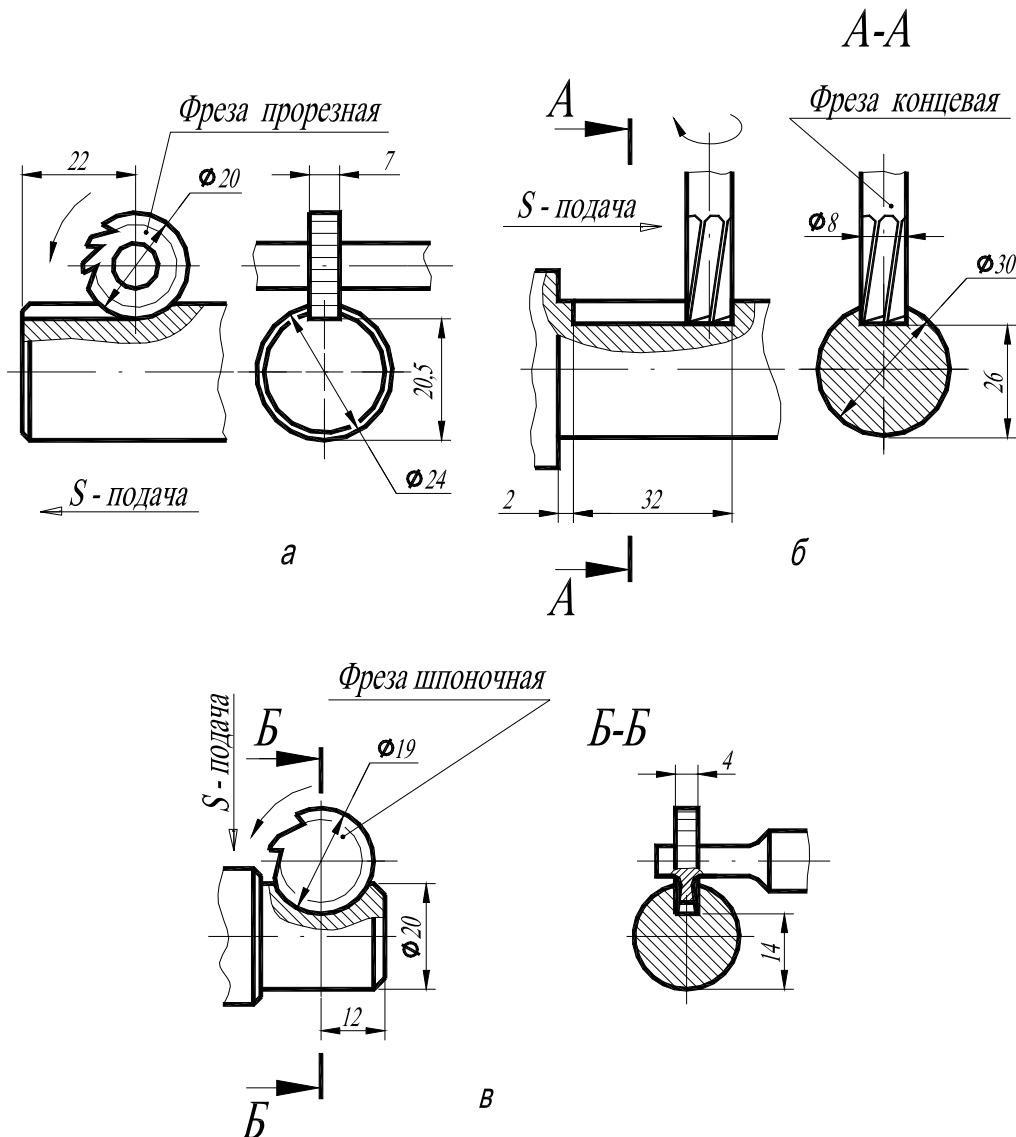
Схемы обработки шпоночных канавок: а – прорезной фрезой; б - концевой фрезой; в – шпоночной фрезой
